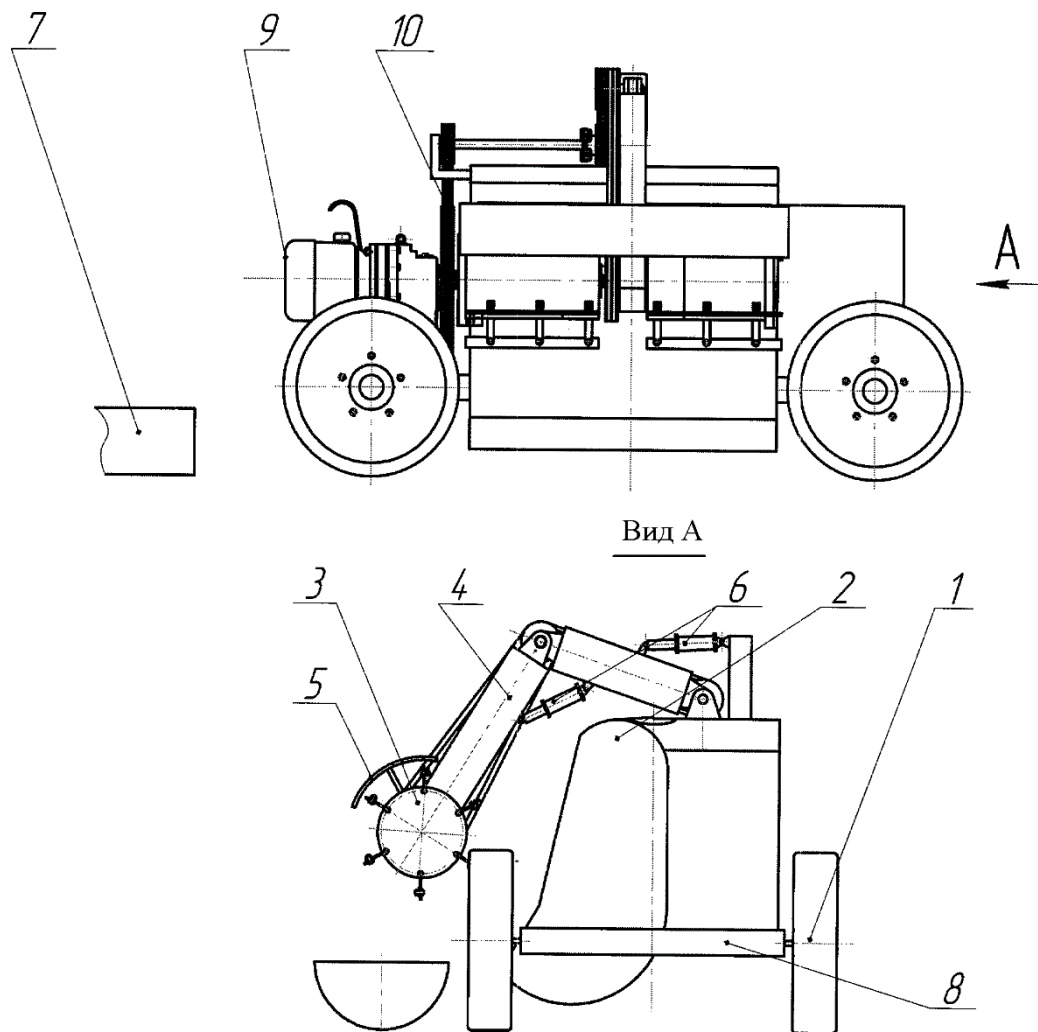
Пристрій для очистки годівниць: 1 – ходова частина; 2 – бункер; 3 – барабан; 4 – стріла; 5 – кожух; 6 – силовий гідроциліндр; 7 – годівниця; 8 – рама; 9 – мотор-редуктор; 10 – передача ремінна.
